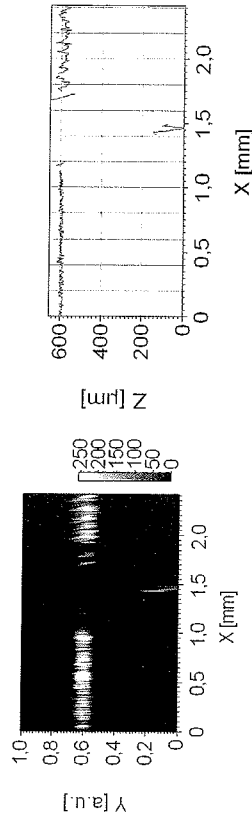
Messung einer Laserschweißnaht mit Fehlstelle.
